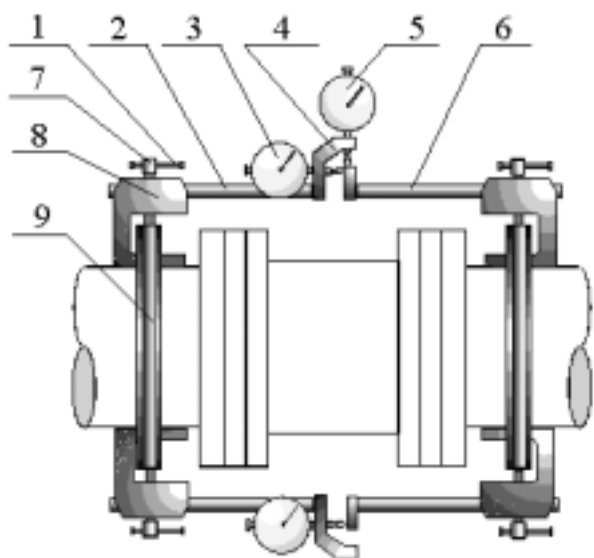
Прибор для центровки ПЦ-4 для зубчатых муфт типа МЗ: 1 – рычаг винта; 2 – штанга с индикаторами; 3–индикатор горизонтальный; 4– стойка; 5 – индикатор вертикальный; 6– штанга с упором; 7– винт; 8– струбцина; 9 – скоба
